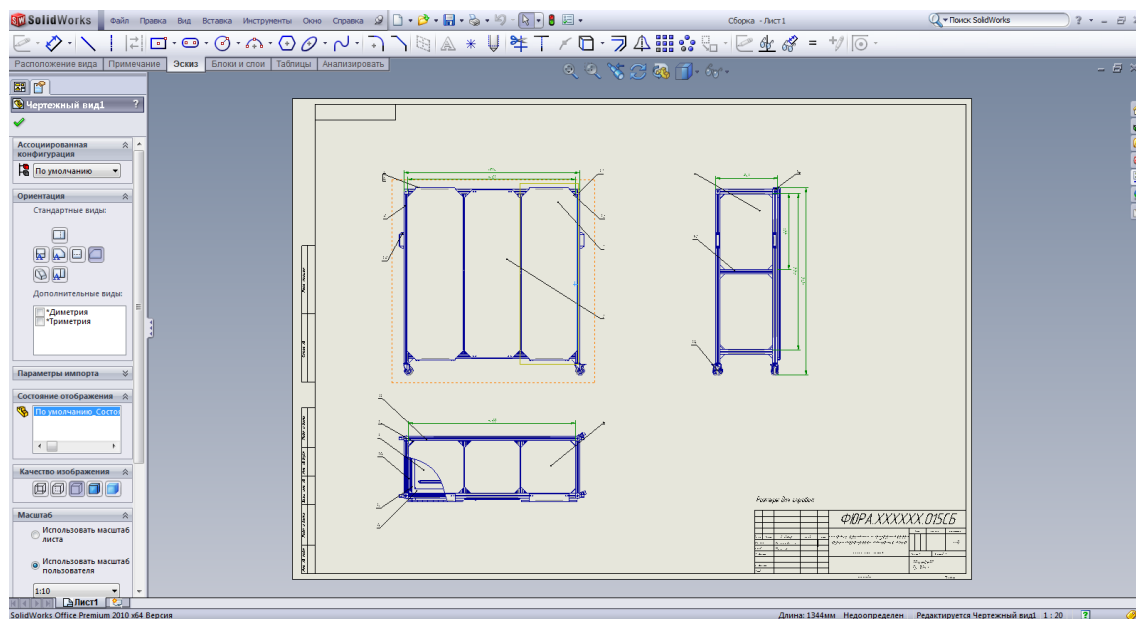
Рабочая среда сборочных чертежей SolidWorks
